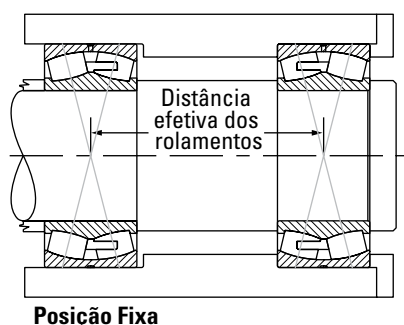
Montagem direta do rolamento autocompensador de rolos.
